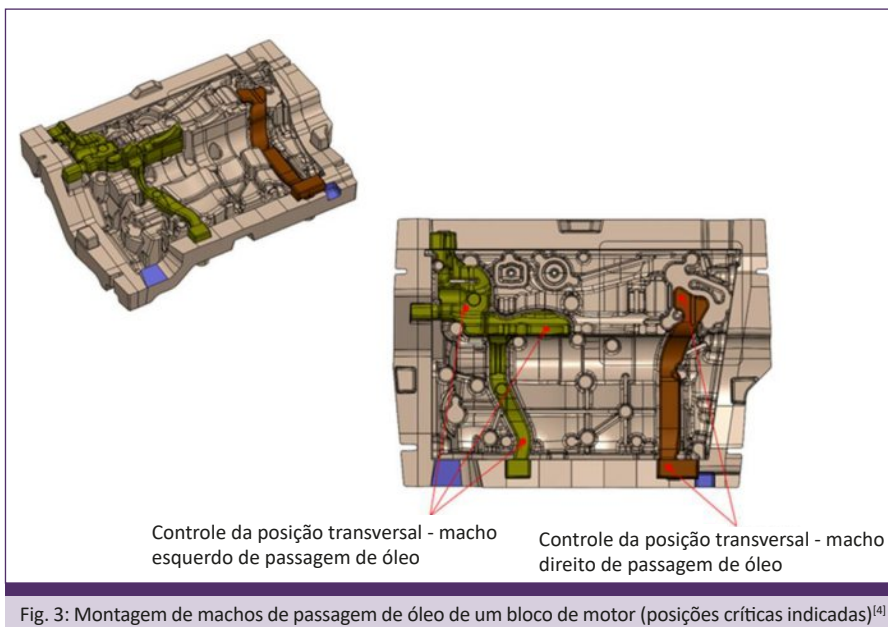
Montagem de machos de passagem de óleo de um bloco de motor (posições críticas indicadas)<sup>[4]</sup>
